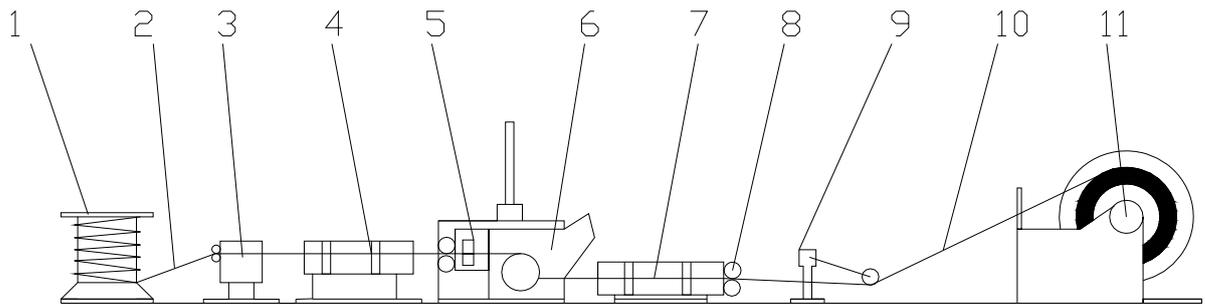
Схема компоновки оборудования линии непрерывного прессования по способу Конформ: 1 – размоточное устройство; 2 – заготовка; 3 – устройство правки заготовки; 4 – устройство очистки заготовки; 5 – гильотинные ножницы; 6 – машина «Conform»; 7 – устройство охлаждения и сушки пресс-изделия; 8 – устройство натяжения пресс-изделия; 9 – устройство контроля натяжения пресс-изделия при его смотке; 10 – пресс-изделие; 11 – намоточное устройство
